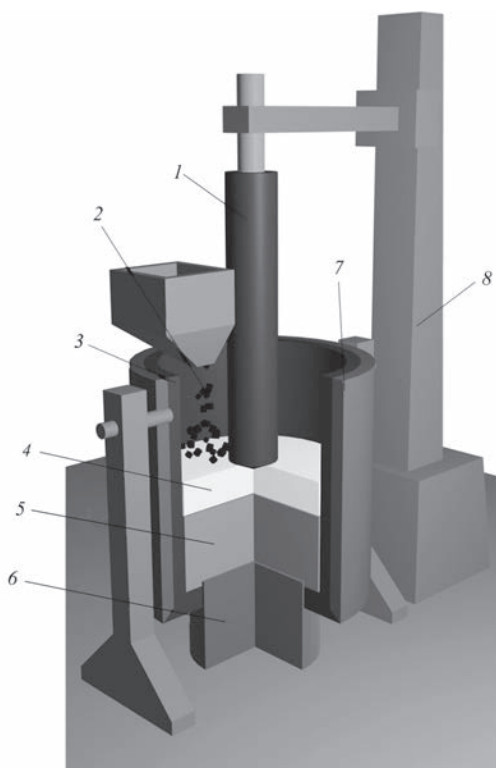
Схема електрошлакового наплавлення міді на сталь: 1 — графітовий електрод; 2 — мідна присадка; 3 — графітовий тигель; 4 — шлакова ванна; 5 — металева ванна; 6 — сталева заготовка; 7 — теплоізоляція; 8 — колонна
